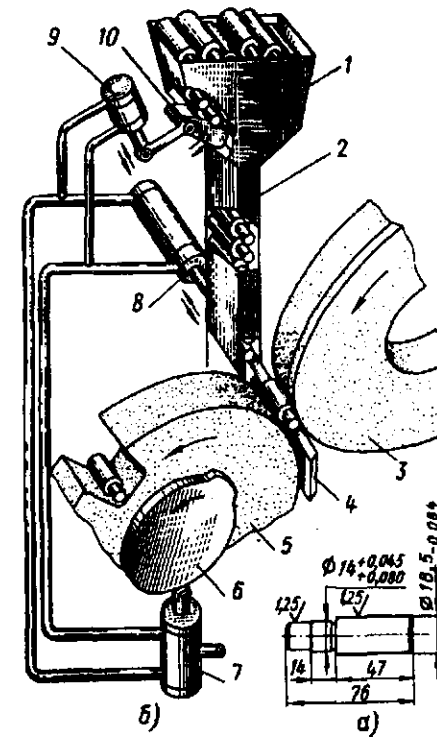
Схемы бункерной автоматической загрузки коротких ступенчатых деталей: а – обрабатываемая деталь; б – схема механизма загрузки
